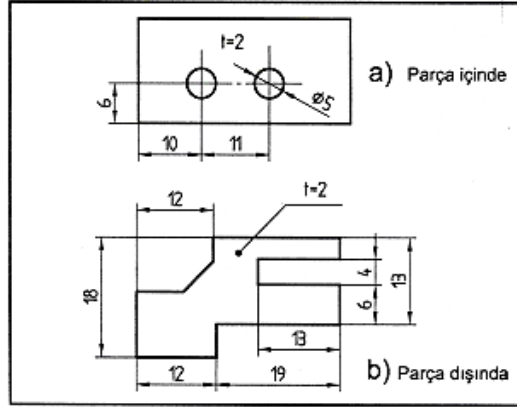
Benzer Parçaların Ölçülendirilmesi
